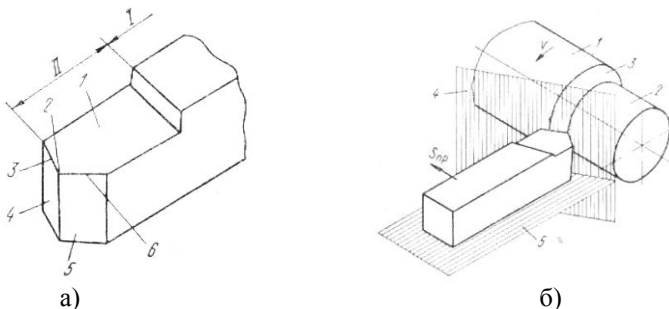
а) части и элементы проходного резца: 1- передняя поверхность; 2-вершина резца; 3-вспомогательное режущее лезвие; 4-вспомогательная задняя поверхность; 5-главная задняя поверхность; 6-главное режущее лезвие. б) координатные плоскости и поверхности обрабатываемой заготовки: 1-обрабатываемая поверхность; 2-обработанная поверхность; 3-поверхность резания; 4-плоскость резания; 5-основная плоскость.
